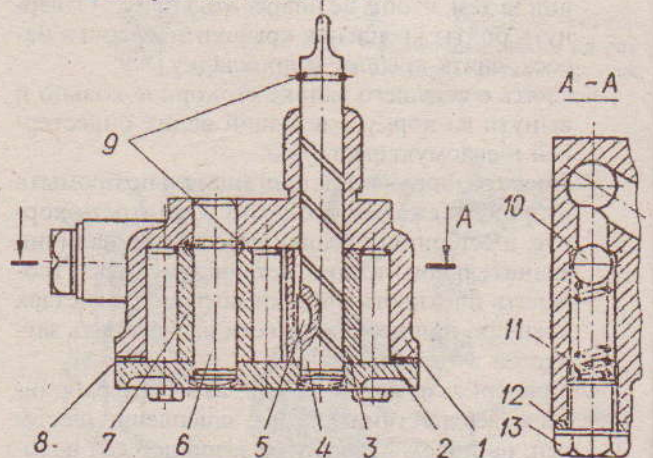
Масляный насос в сборе: 1 - корпус; 2 - крышка в сборе; 3 - шестерня ведущая; 4 - ведущий валик; 5 - сегментная шпонка; 6 - ось ведомой шестерни; 7 - шестерня ведомая; 8 - прокладка крышки; 9 - кольцо стопорное осей ведомой и ведущей шестерен; 10 - шарик редукционного клапана; 11 - пружина редукционного клапана; 12 - прокладка пробки редукционного клапана; 13 - пробка редукционного клапана
